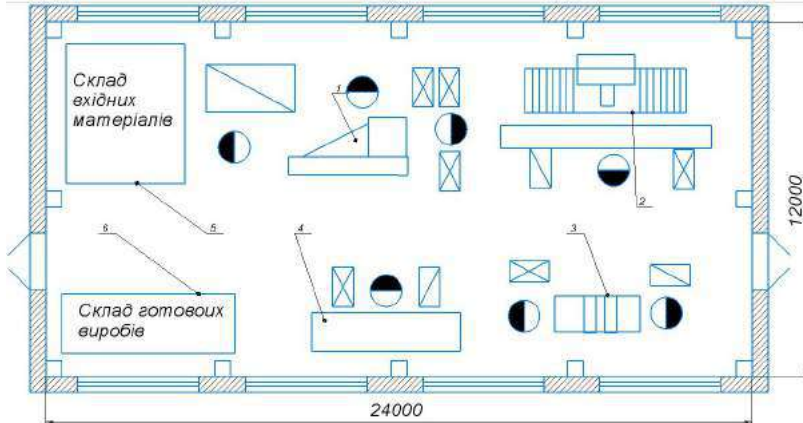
Планування цеху зі створення фасадну №3МЩ
